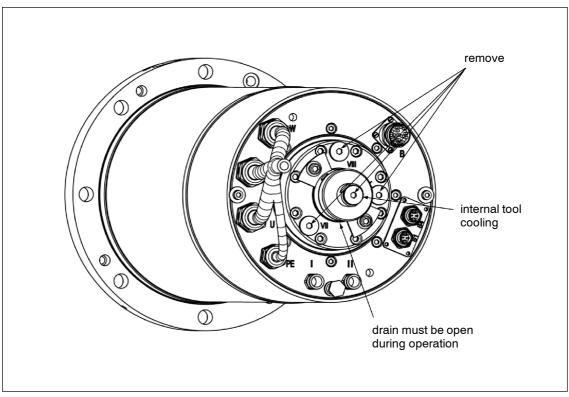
ECS-M idraulico 2SP120 -1H 3 - con distributore rotante
